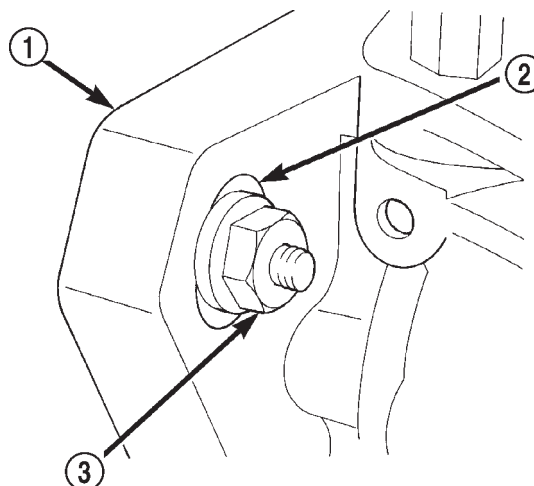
Montage der Ausbauwerkzeuge für das Antriebszahnrad
